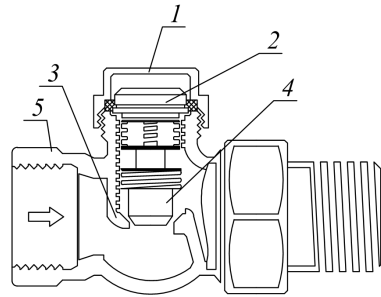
Схема запорно-регулирующего клапана: 1 – защитный колпачек; 2 – винт предварительной настройки; 3 – седло клапана; 4 – рабочий конус клапана; 5 – седло клапана
